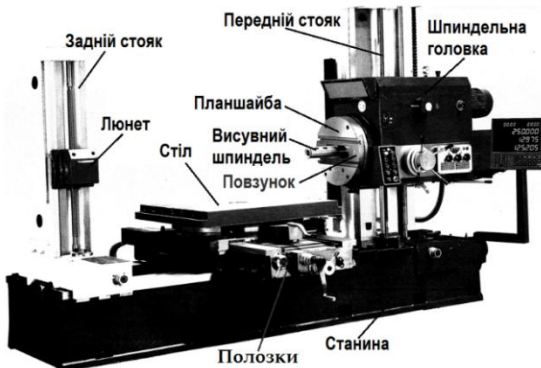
Горизонтально-розточувальний верстат (легкий)
